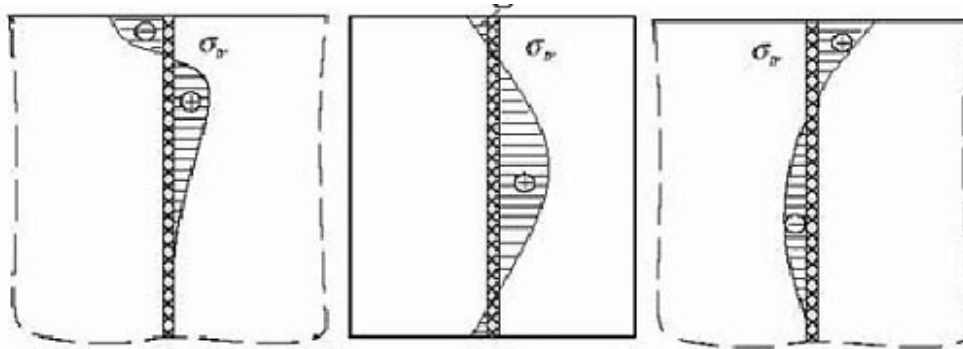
Tensiones transversales a lo largo del cordón de soldadura.
